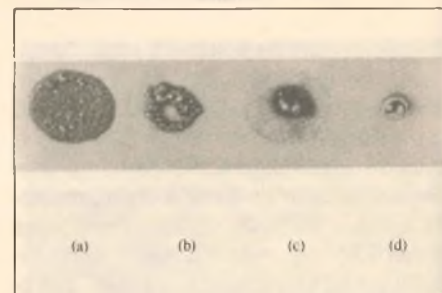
Teste de bolota de solda em quatro pastas aplicadas a um substrato de alumina. (a) soldabilidade extremamente baixa (b) soldabilidade muito baixa (c) soldabilidade baixa (d) soldabilidade boa
